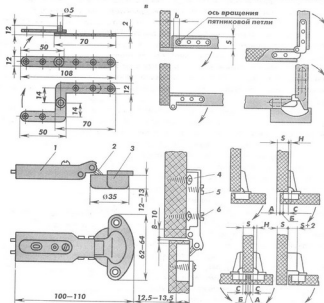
Виды петель для навески откидных и распашных дверей и схемы установки дверей на петли (продолжение):
